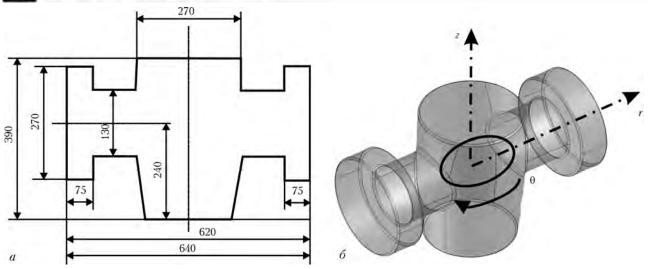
Заготовка корпуса фланцевой задвижки с условным проходом 80 мм: $a-\,$ эскиз; $6-\,$ изометрия
